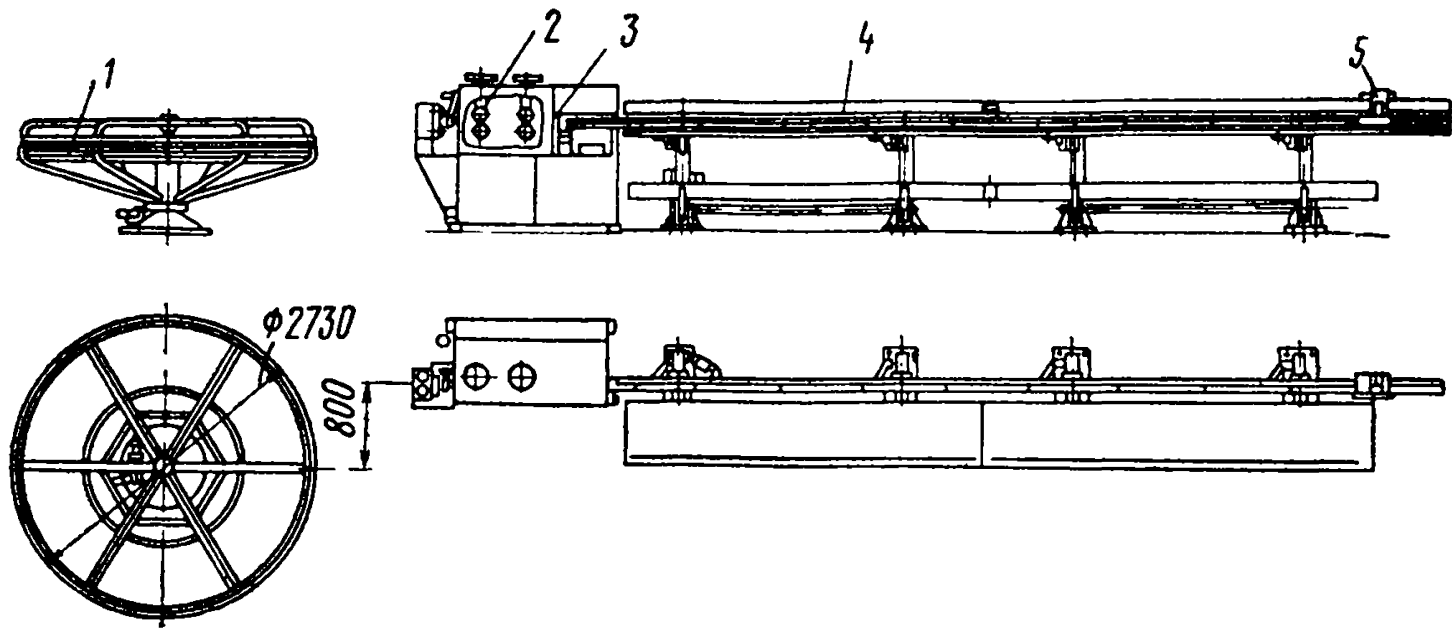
Линия заготовки проволоки и прядей СМЖ-213
